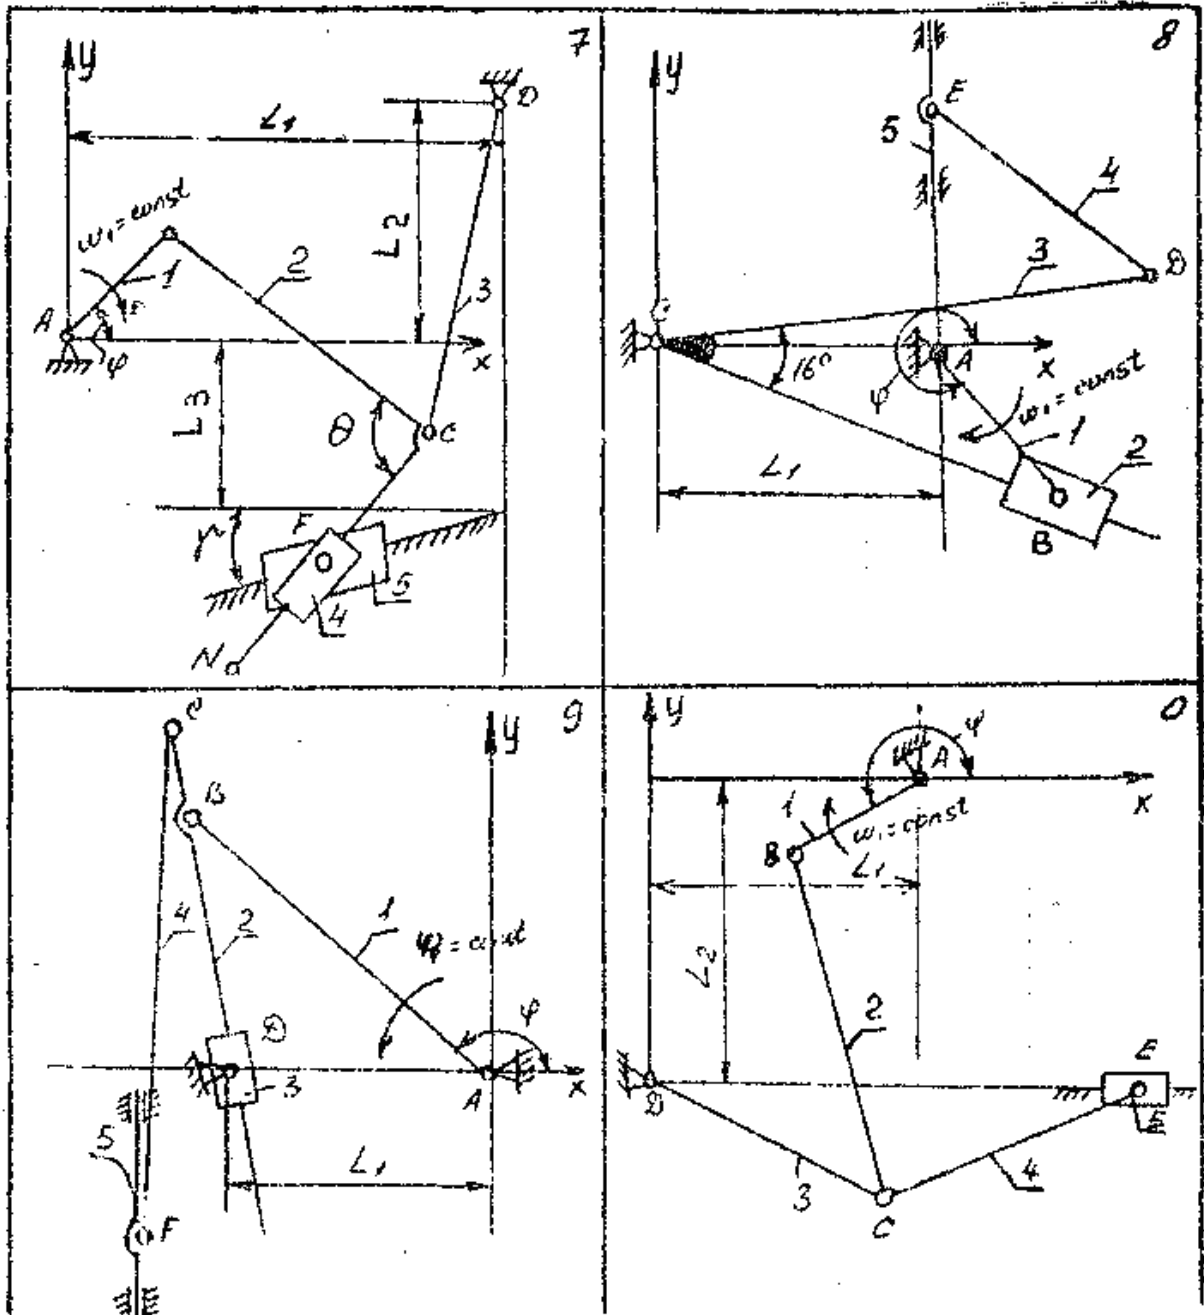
Кинематическая схема шарнирно-рычажного механизма рабочей машины (окончание)
